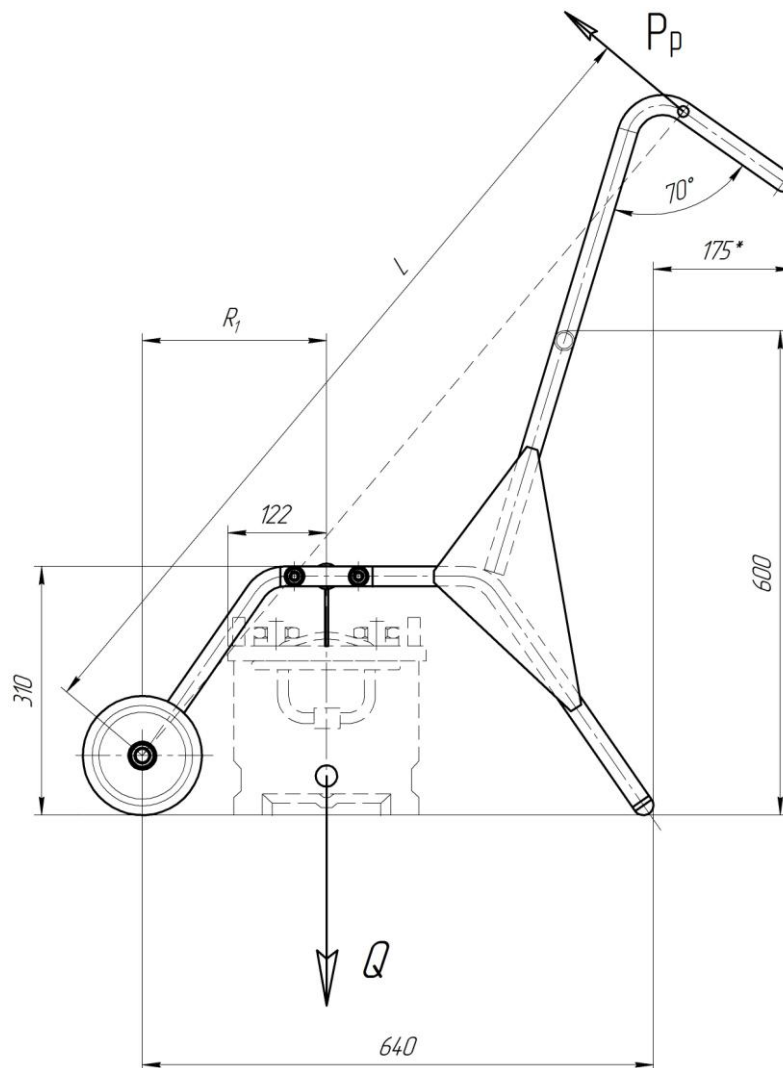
Схема к расчету усилия на рукоятки
